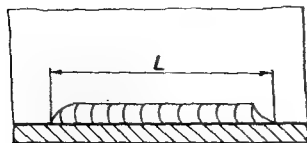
Modo de indicar la longitud L de un segmento de soldadura.
